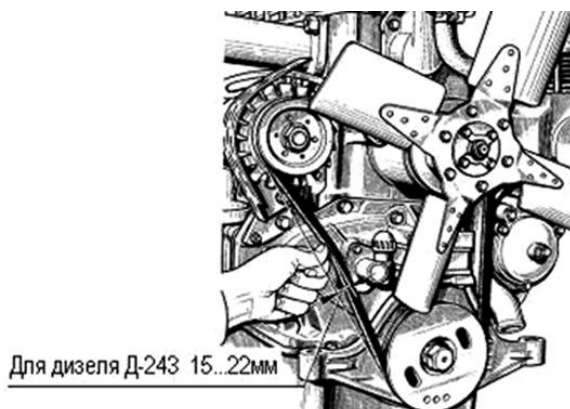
Проверка натяжения ремня вентилятора
